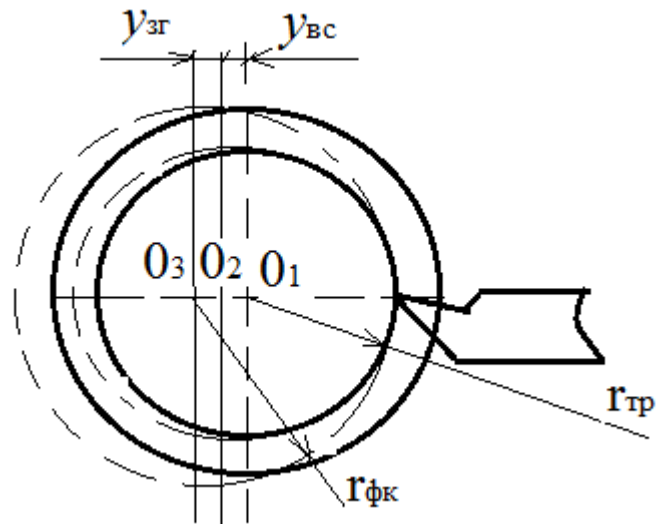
Вплив на розмір деталі зміщення осі через відтиски верстату і заготовки
